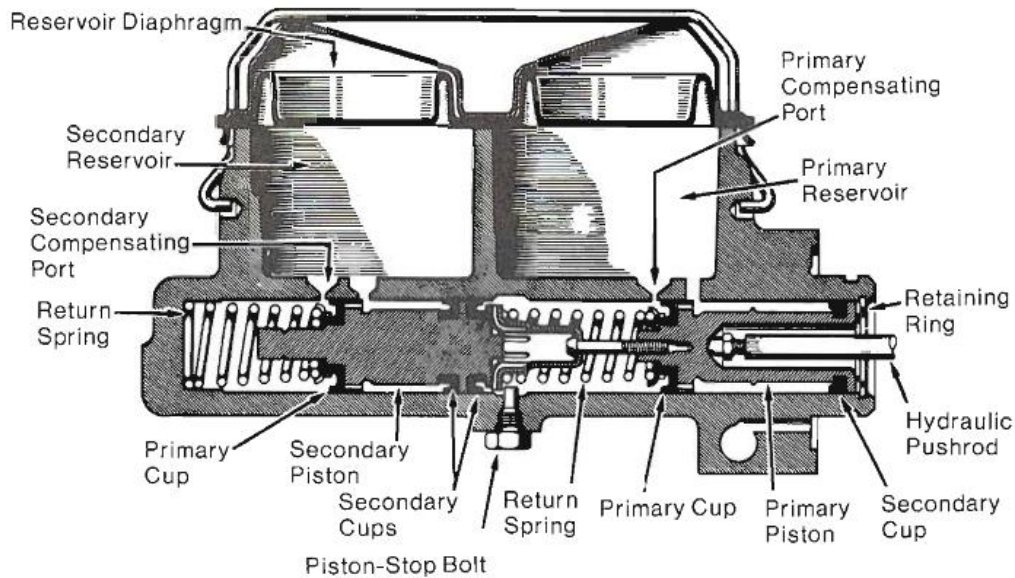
Componentes de um Tandem Master Cylinder [2]
